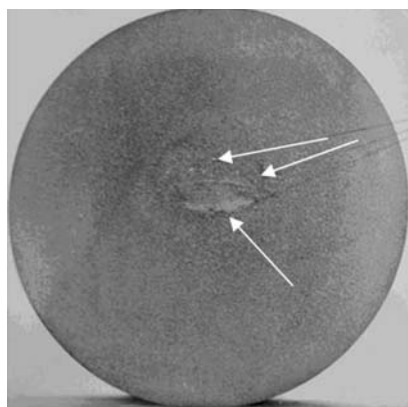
Фото макрошлифа в поперечном сечении заготовки черновой оси колесной пары: дефекты литья указаны стрелками
